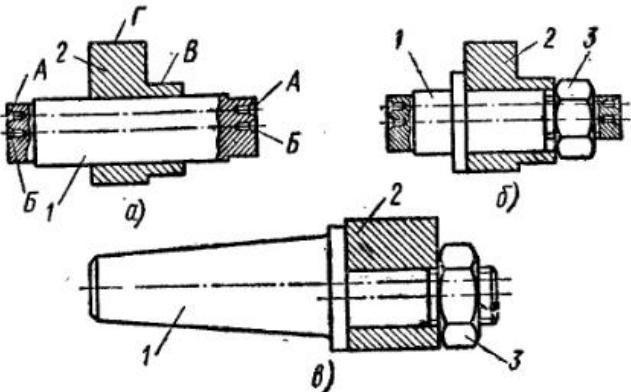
Оправки для обработки эксцентриковых заготовок:
